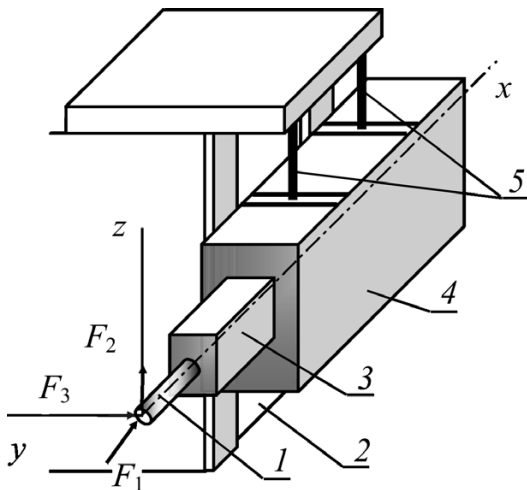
Схема нагружения корпуса шпиндельной бабки:
